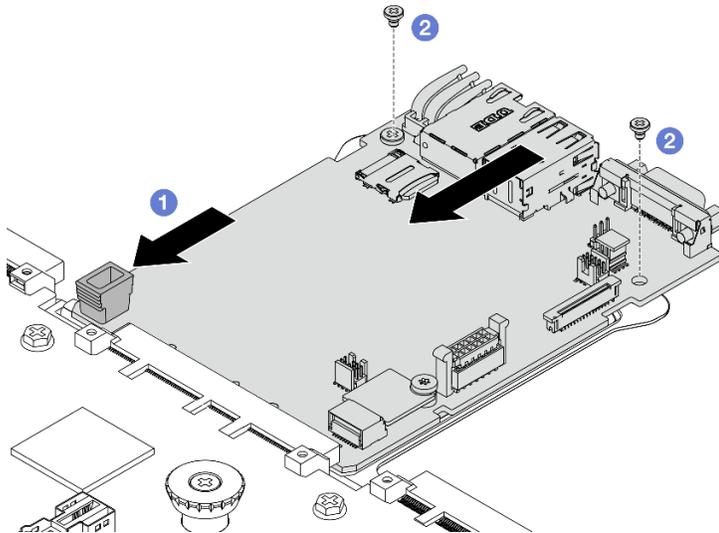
Instalando a placa de E/S do sistema na placa do processador
